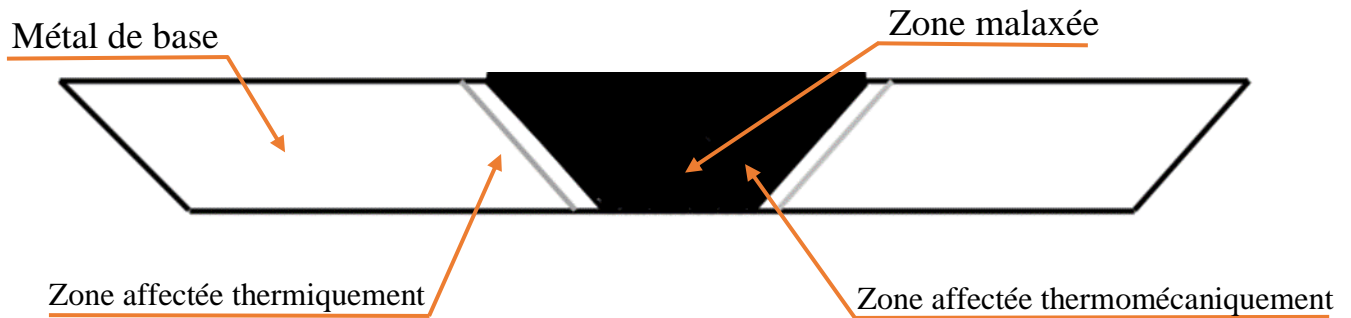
Zones principales d'un cordon de soudure par FSW
